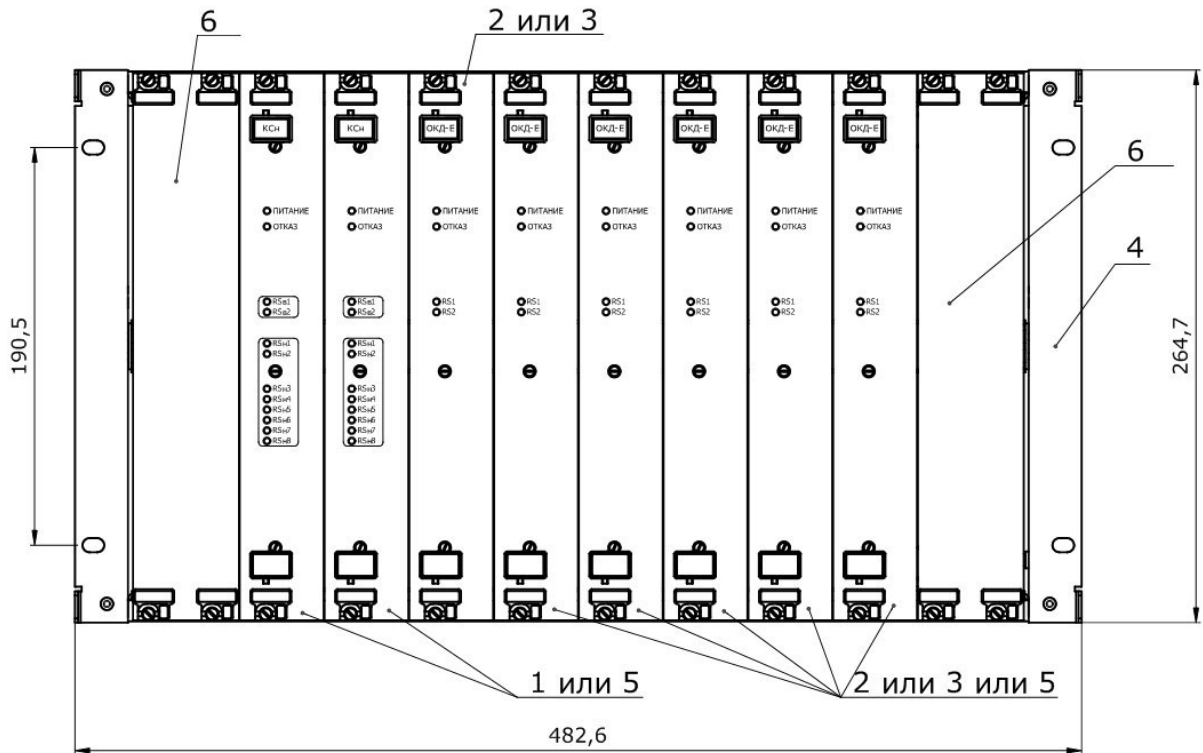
Габаритные размеры АОД ЕИУС.465275.002-03
